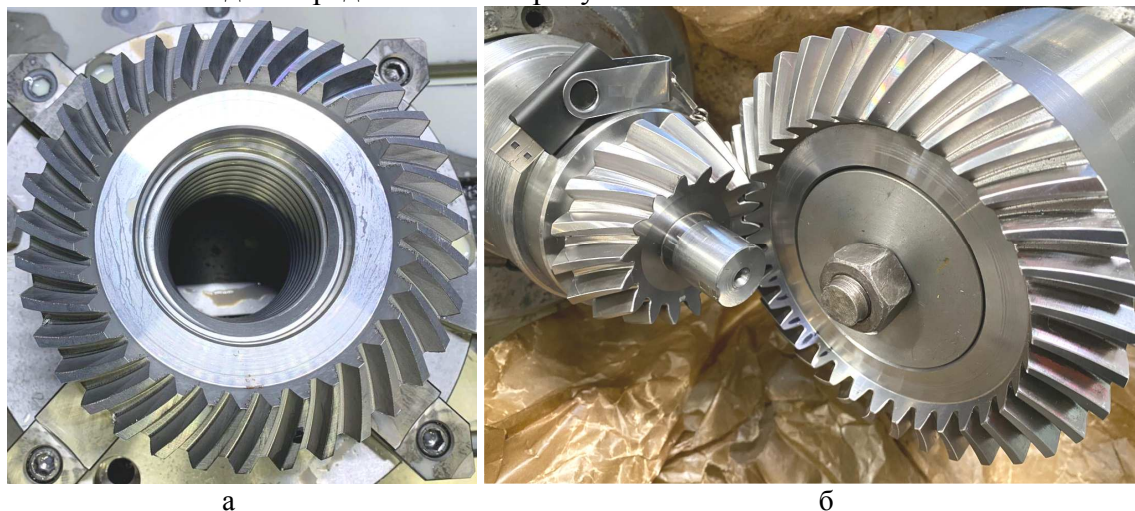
Изготовленные образцы зубчатого колеса (а) в паре с шестерней (б)
